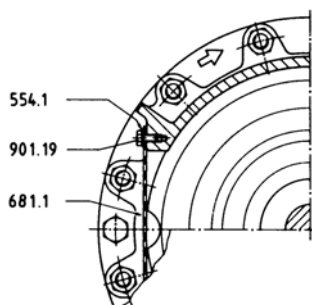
Befestigung des Schutzblechs an der Antriebslaterne
